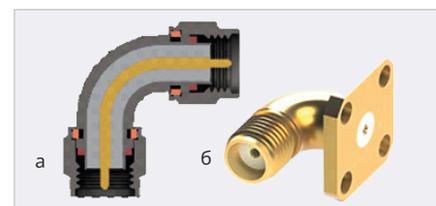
Схематическое изображение угловых соединителей третьего конструктивного исполнения (а), внешний вид вывода энергии SMA № 3457-1 (б)
